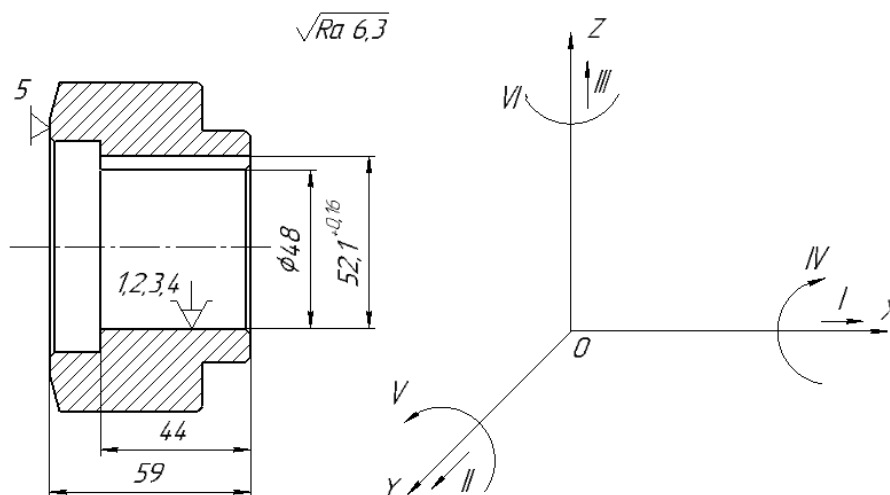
Схема базування заготовки 3-х кулачковому патроні
